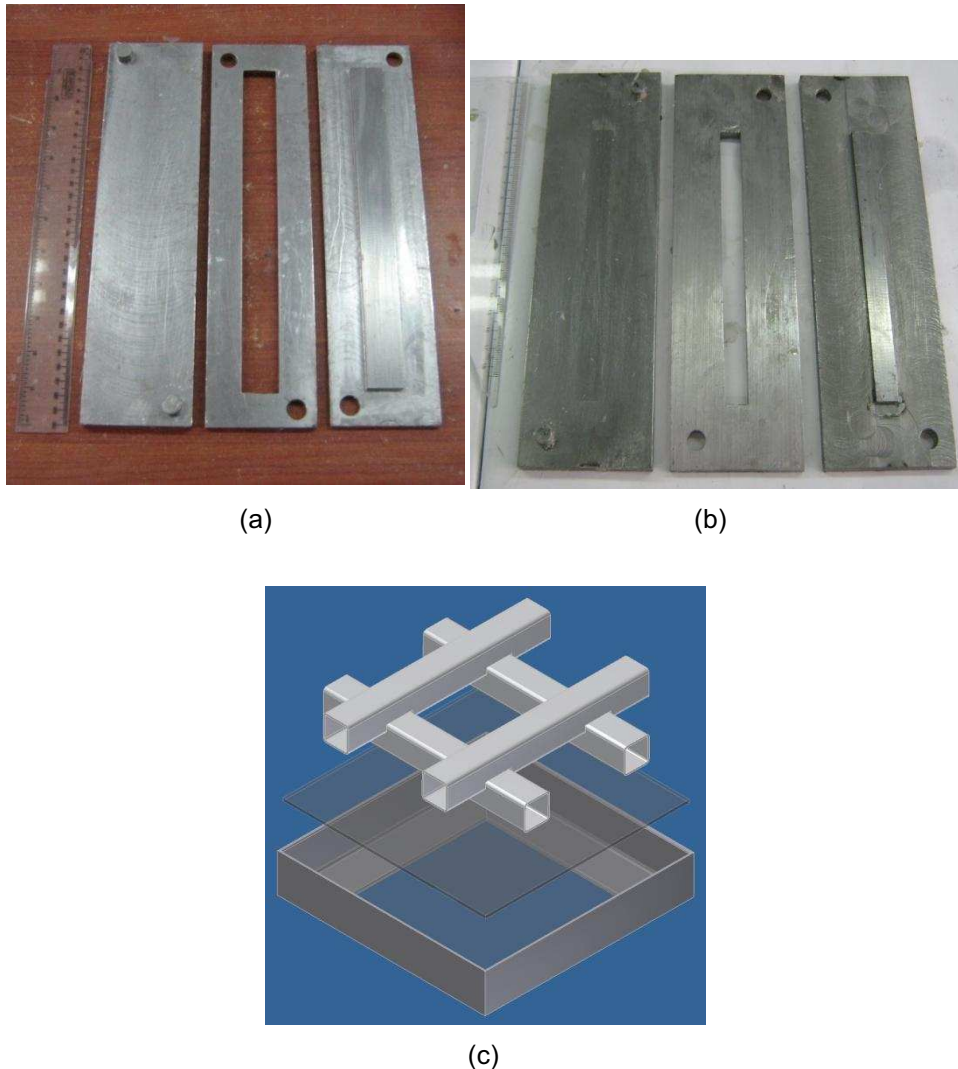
(a) Molde de tracción. (b) Molde de flexión. (c) Molde de impacto.
